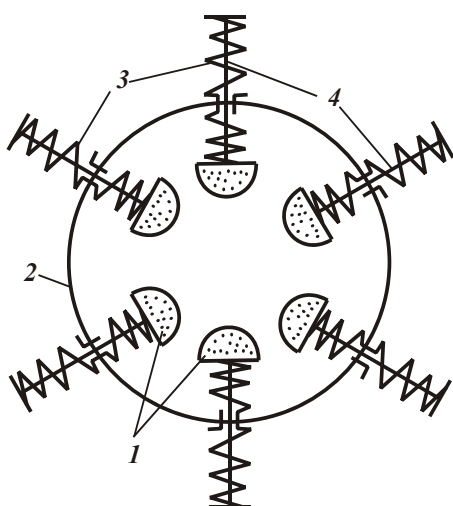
Инструмент для шлифования наружных поверхностей: 1 – шлифовальный брусок; 2 – корпус цилиндрический; 3 – пружина; 4 – штырь.
